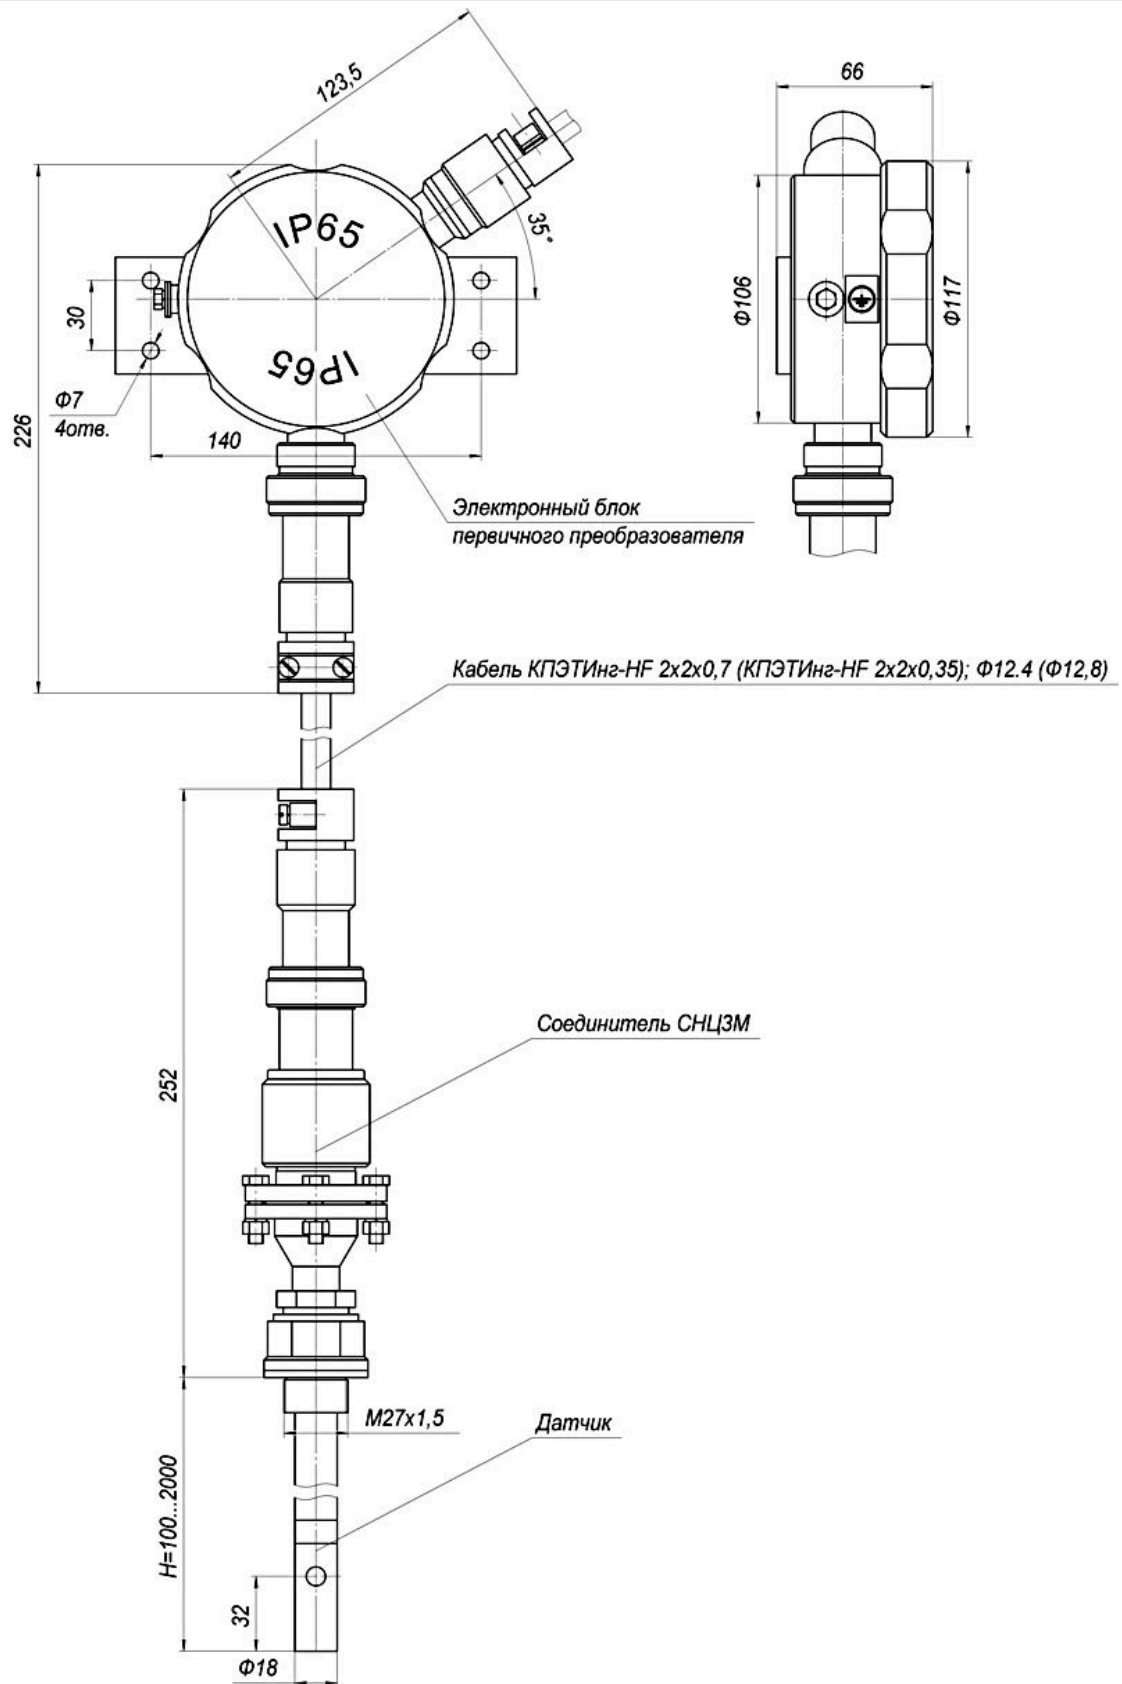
Габаритные, установочные и присоединительные размеры первичного преобразователя погружного типа с разнесенными электронным блоком и датчиком
